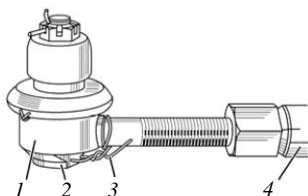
Проверка люфта в шарнирах рулевой тяги:
